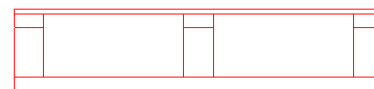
Desain Awal Pallet Penyimpanan Tampak Bawah
